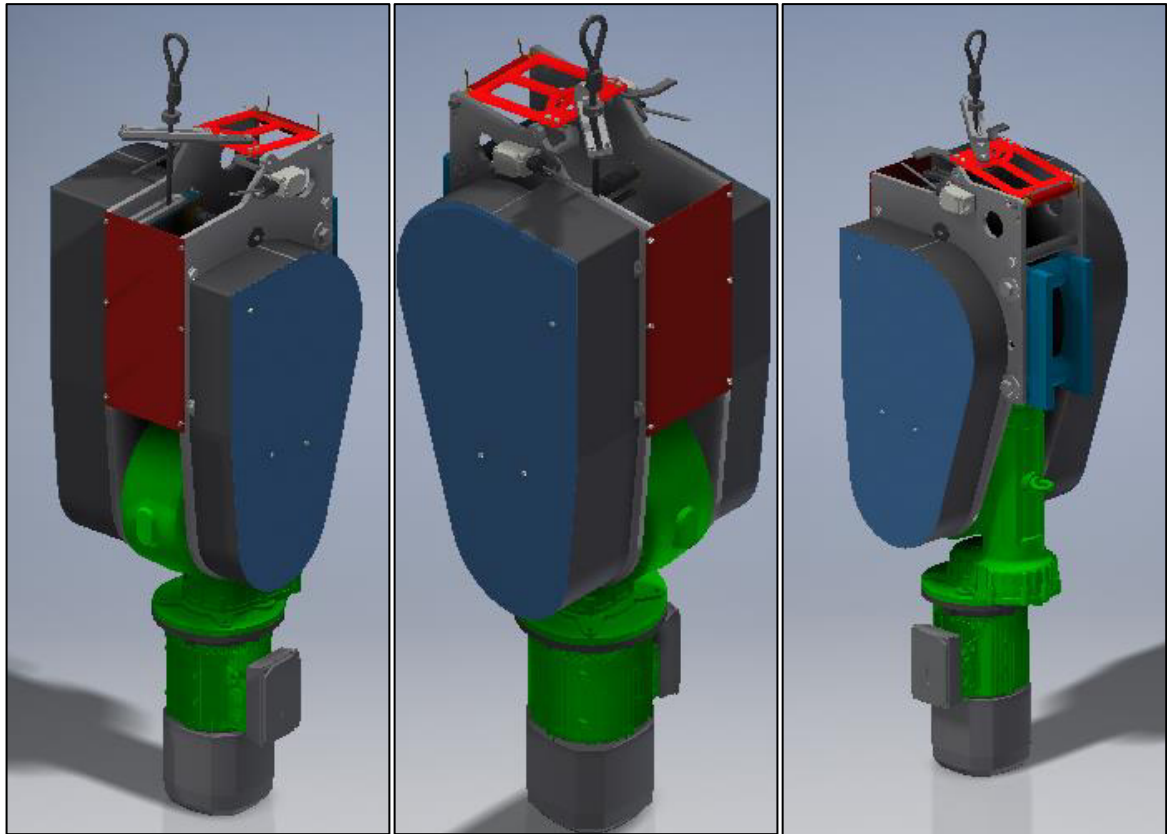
Desenho em CAD 3D do mecanismo sobe e desce 2000 kg.
